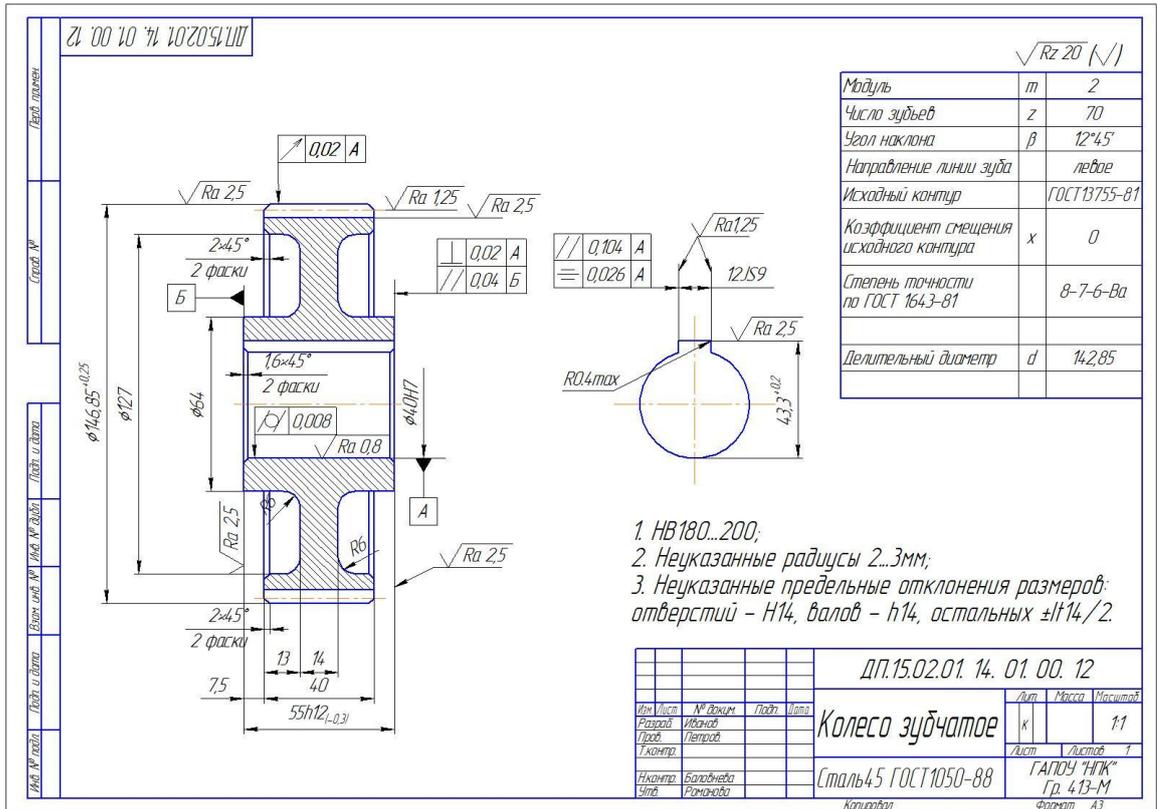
Пример выполнения чертежа детали «Колесо зубчатое»
